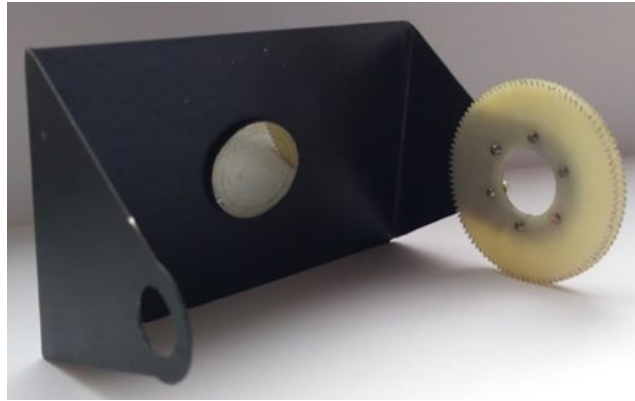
Зовнішній вигляд шторки КріоАТП
